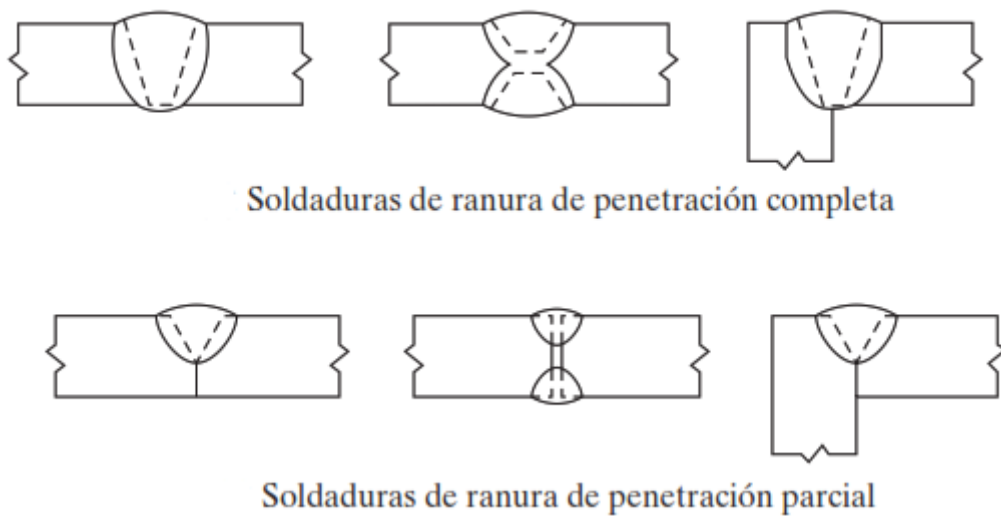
Soldadura de ranura (McCormac & Csernak, 2012)
